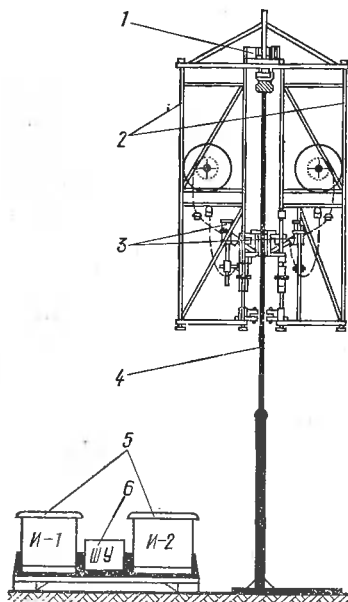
Схема установки «Циркоматик» для сварки горизонтальных швов порошковой проволокой:
